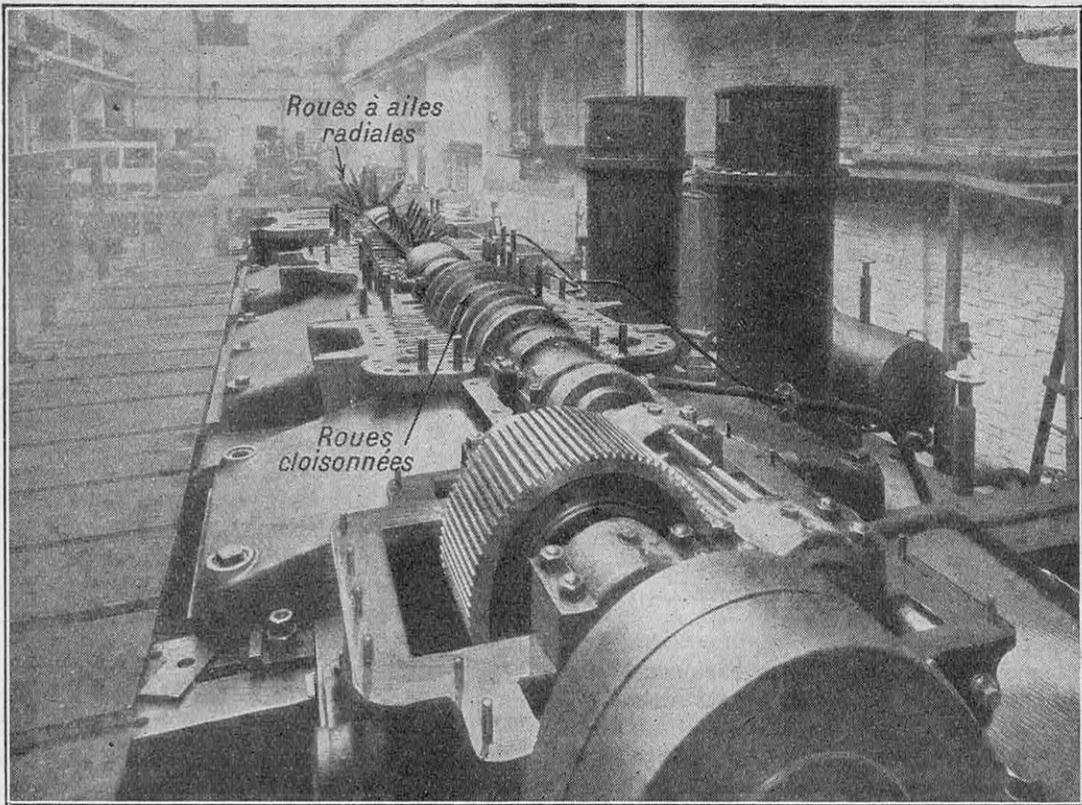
VUE, PRISE DU CÔTÉ DES ROUES CLOISONNÉES, DE LA MACHINE RATEAU
